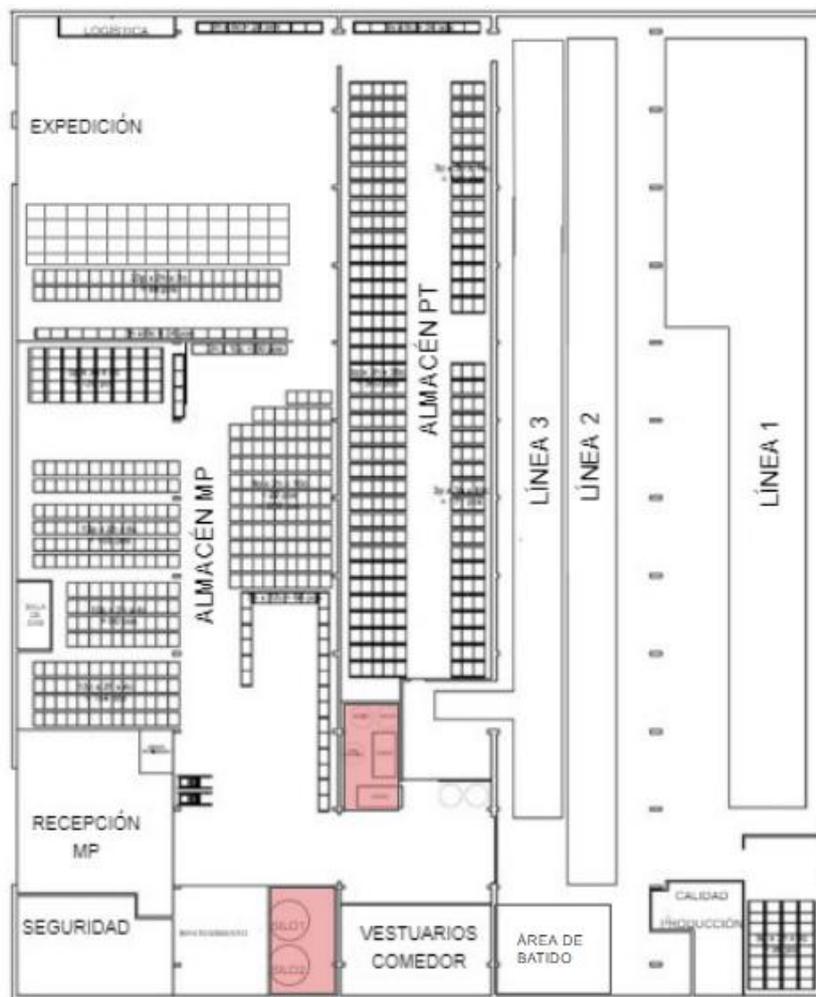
Layout de la planta con área de almacenamiento de MP en silos cisternas y tanques sombreada en rojo
